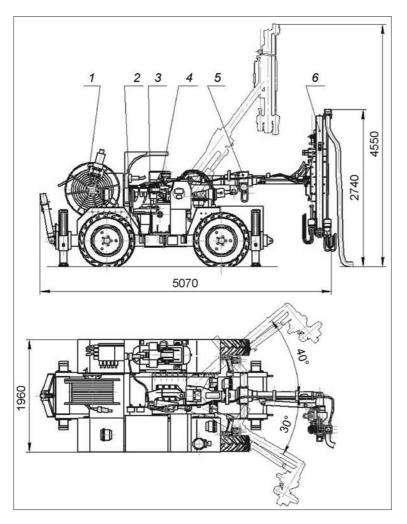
Конструктивная схема установки для возведения крепи УВК-5С: I — барабан в сборе; 2 — часть ходовая; 3 — управление; 4 — гидросистема; 5 — манипулятор; 6 — машина бурильная
